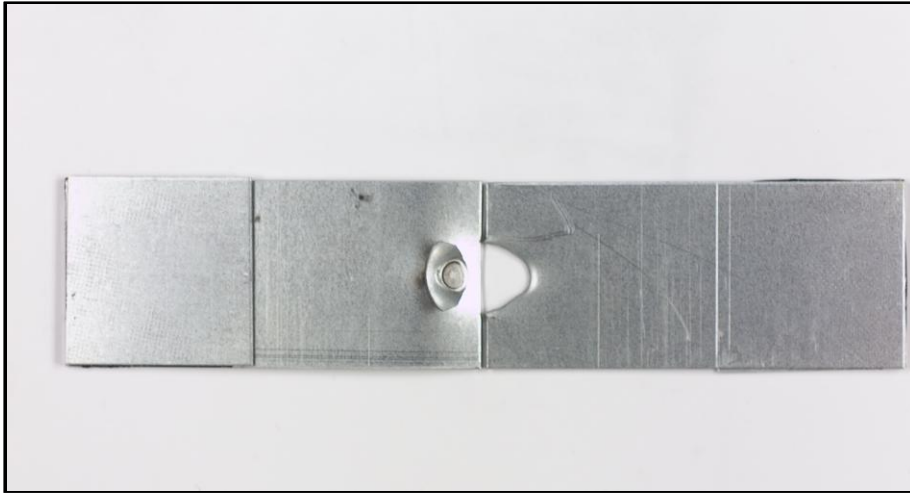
Eprouvette soudée par point après l'essai de traction de l'acier TRIP 700-1,4mm
